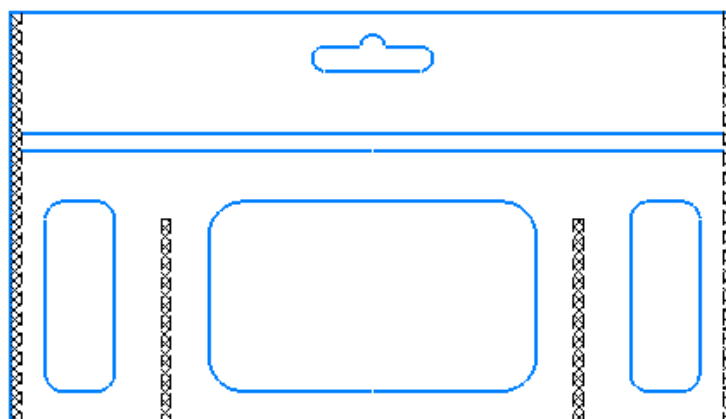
Готовий пакет після формування, зварювання, вварювання зіп-застібки та висічки єврослоту, штриховкою позначено зварні шви.
